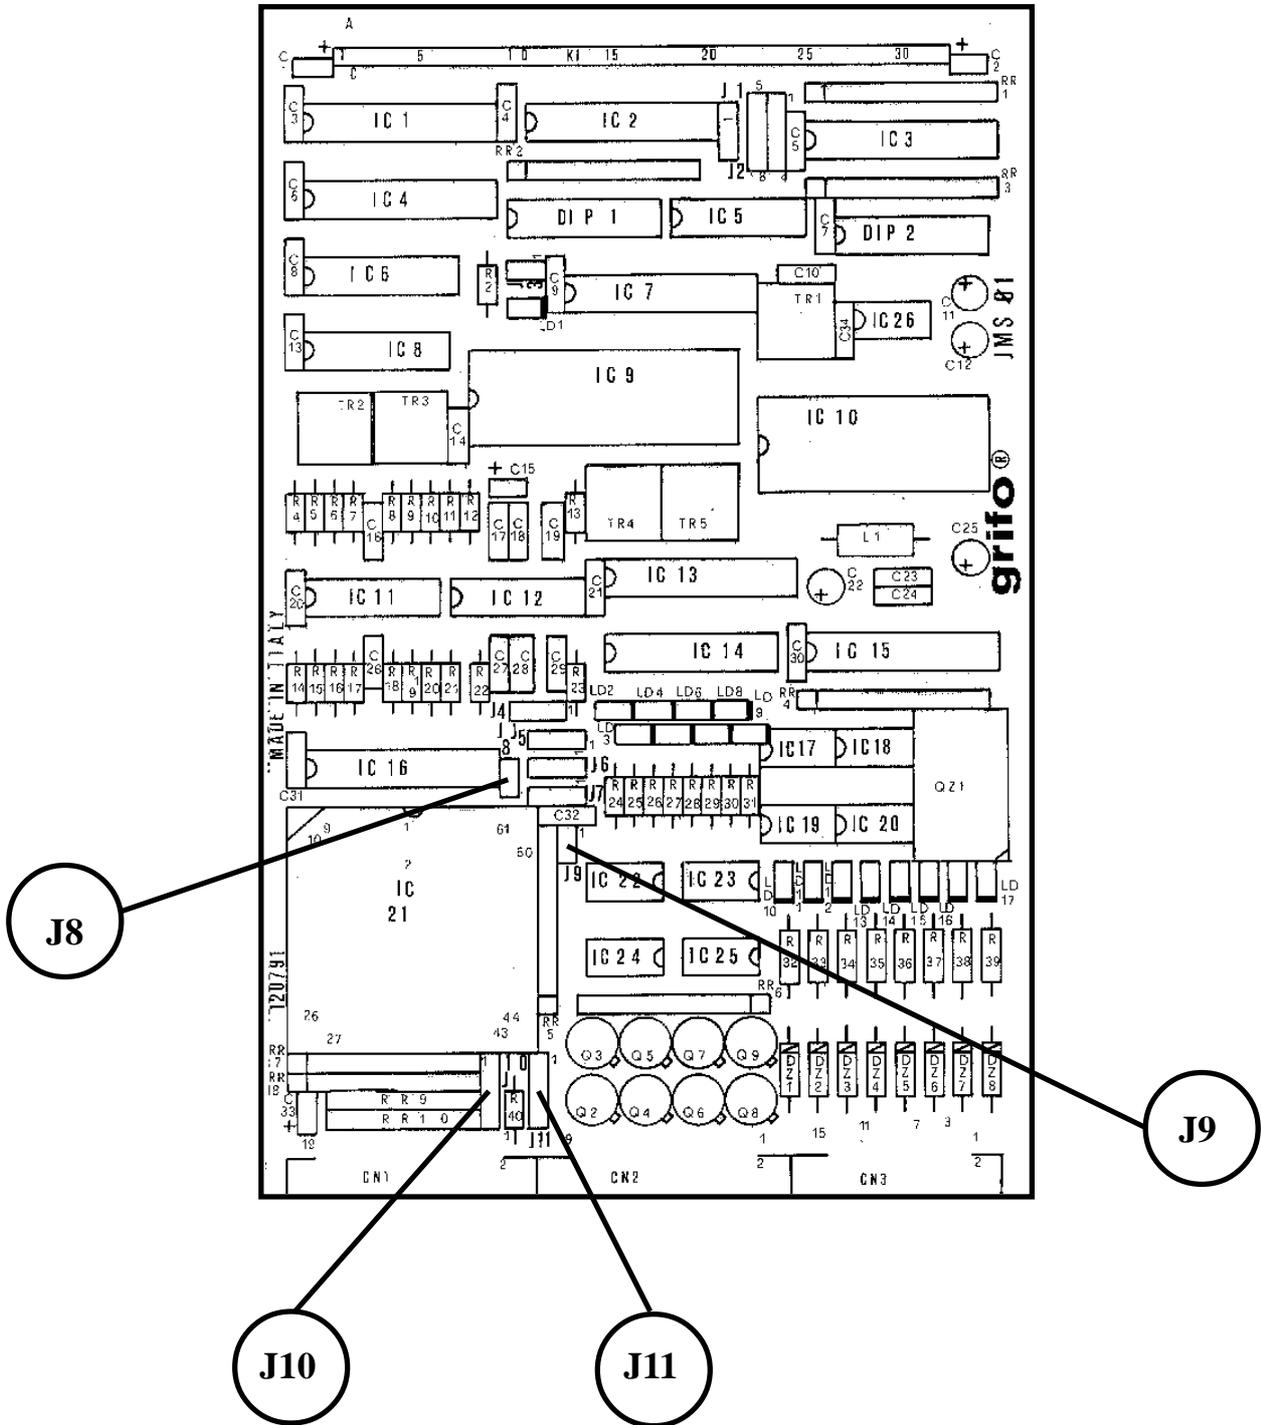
DISPOSIZIONE JUMPERS PER THCT 12316
